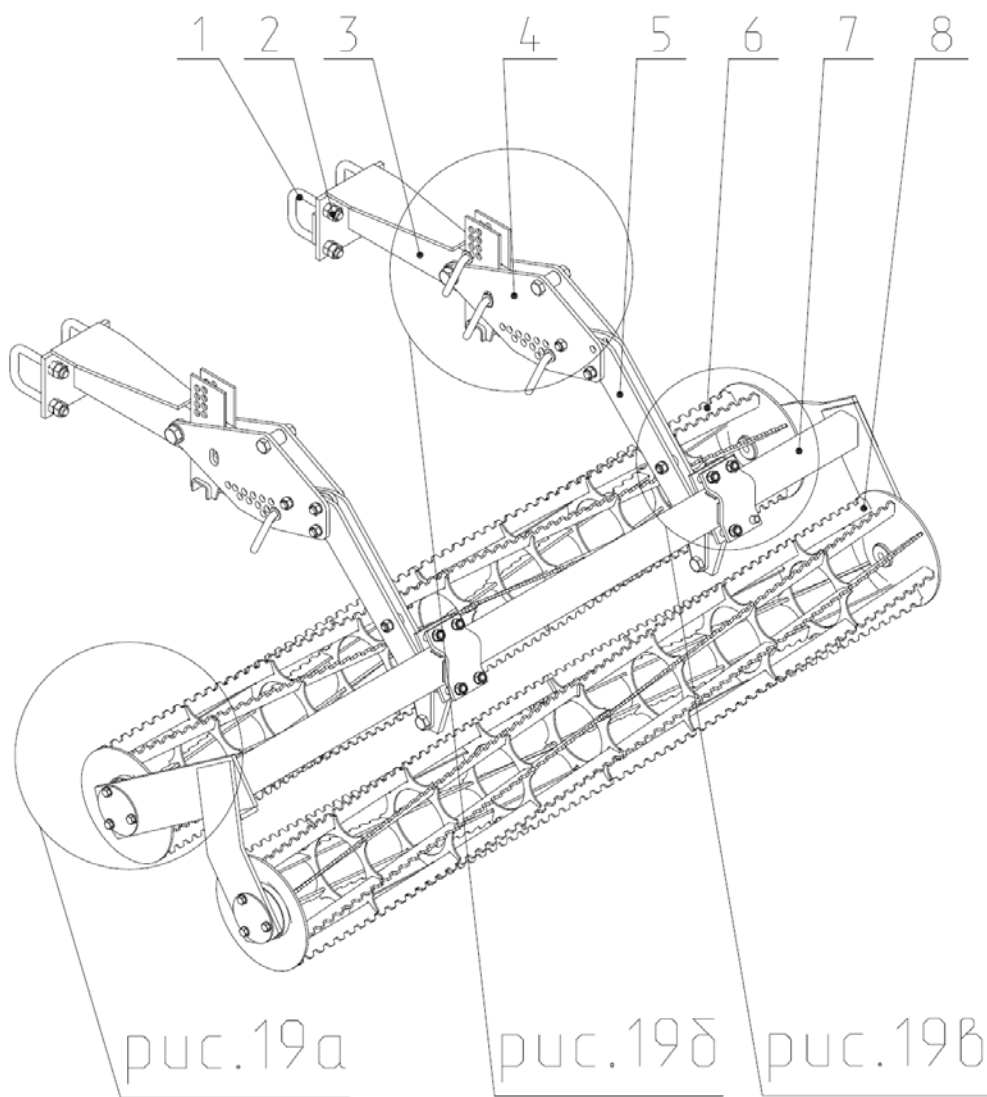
КСП 04.000А Каток прикатывающийся 2-х рядный.
